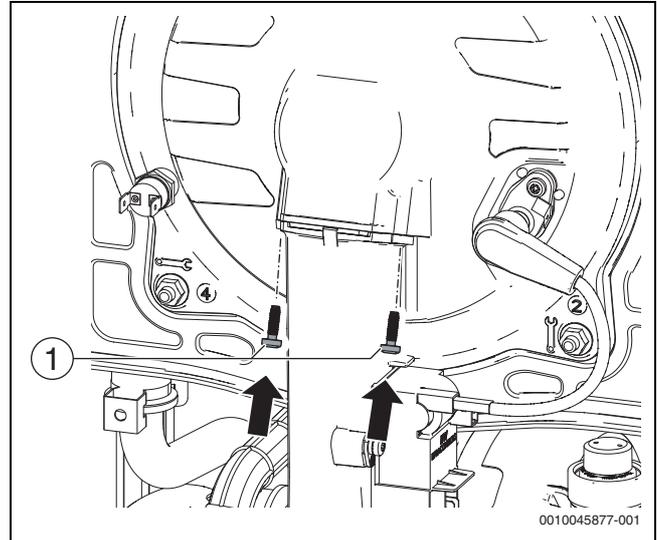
Montaje de los tornillos en la puerta de la cámara de combustión
